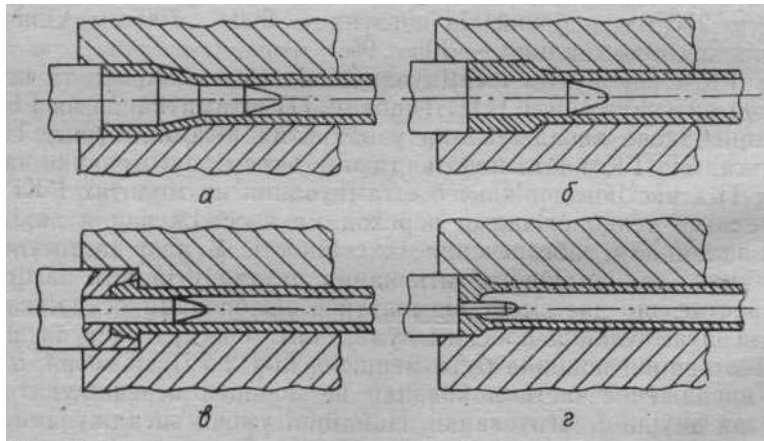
Висадка потовщень різної форми на трубних заготовках
